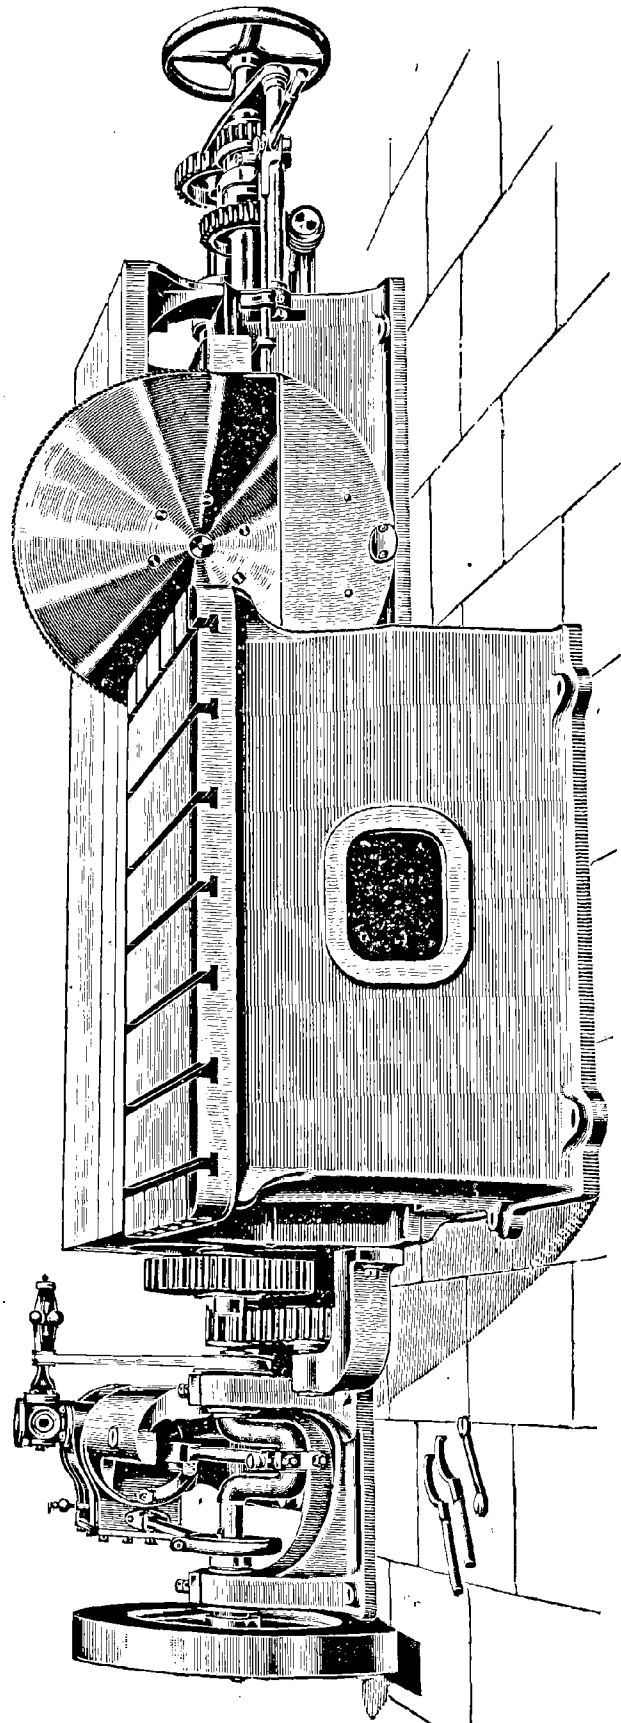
Machine à scier les métaux à lano circulaire directement actionnée par une machine à vapeur.
